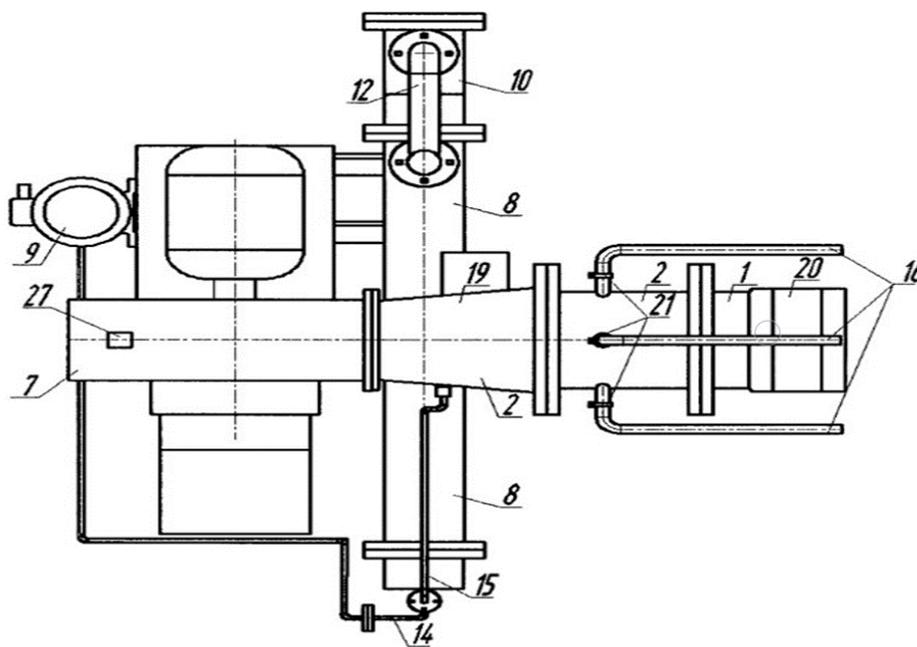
Общий вид мазутной горелки сверху [28]
